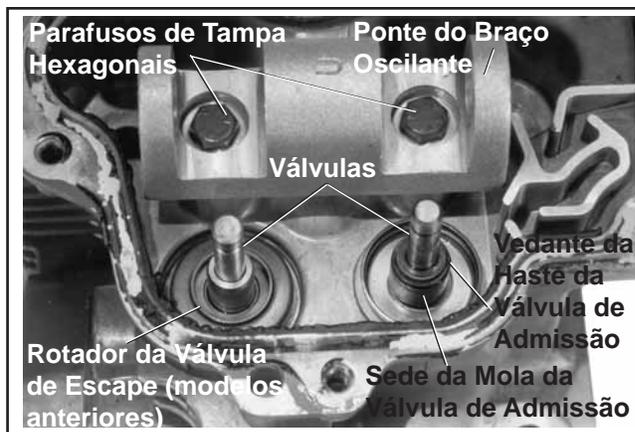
Instalar a Ponte Oscilante e as Válvulas.
